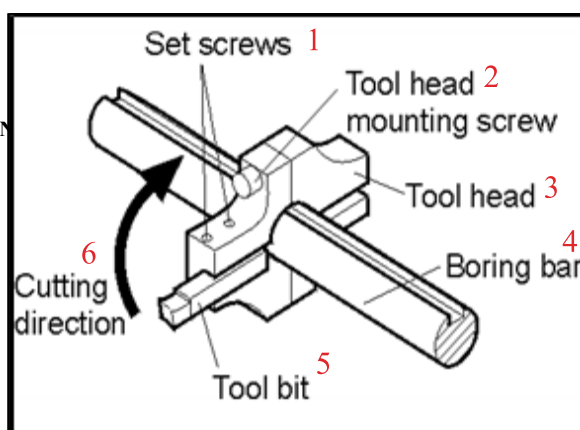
INSTALLATION DU PORTE-OUTIL
